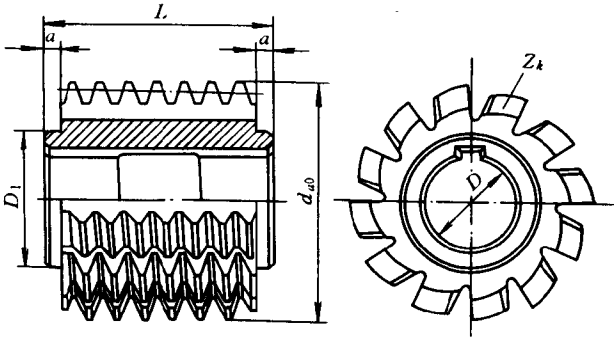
整体高速钢齿轮滚刀的结构形式
